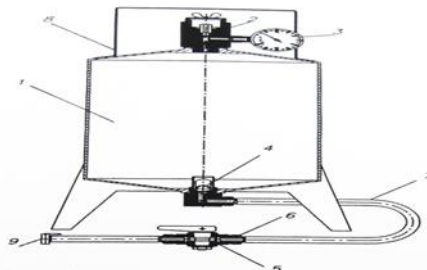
установка для заправки тормозной жидкости в гидропривод сцепления автомобиля КАМАЗ
